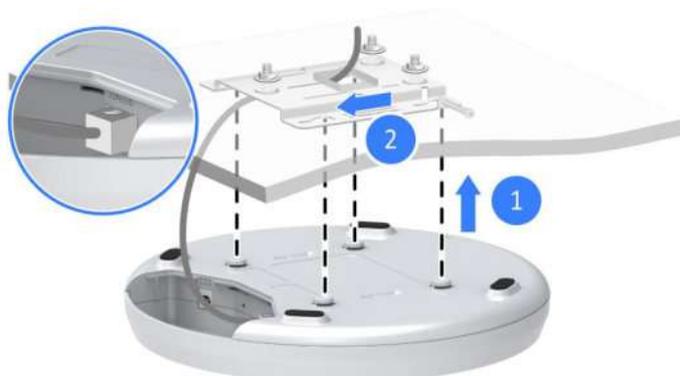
Asegure el Dispositivo al Soporte de Montaje
